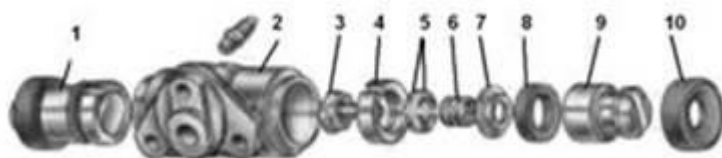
Детали колесного цилиндра: 1 — поршень в сборе; 2 — корпус цилиндра; 3 — упорный винт; 4 — упорное кольцо; 5 — сухари; 6 — пружина; 7 — опорная чашка; 8 — уплотнитель; 9 — поршень; 10 — защитный колпачок.
